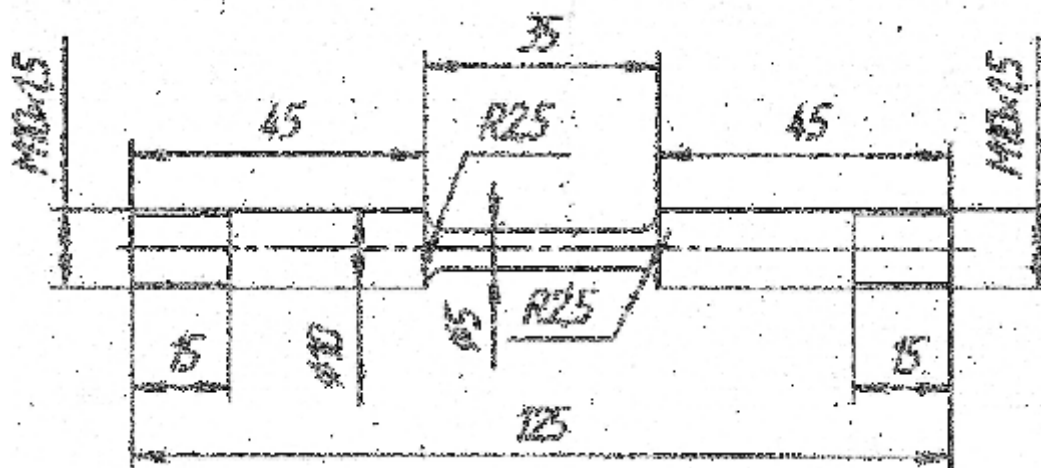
Образец для испытаний на GleebleSystem3800
